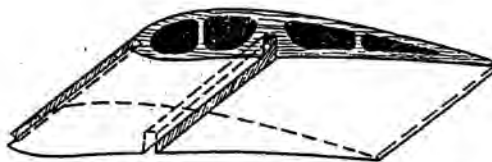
Der geteilte Holzblock mit den ausgearbeiteten Erleichterungsaussparungen
